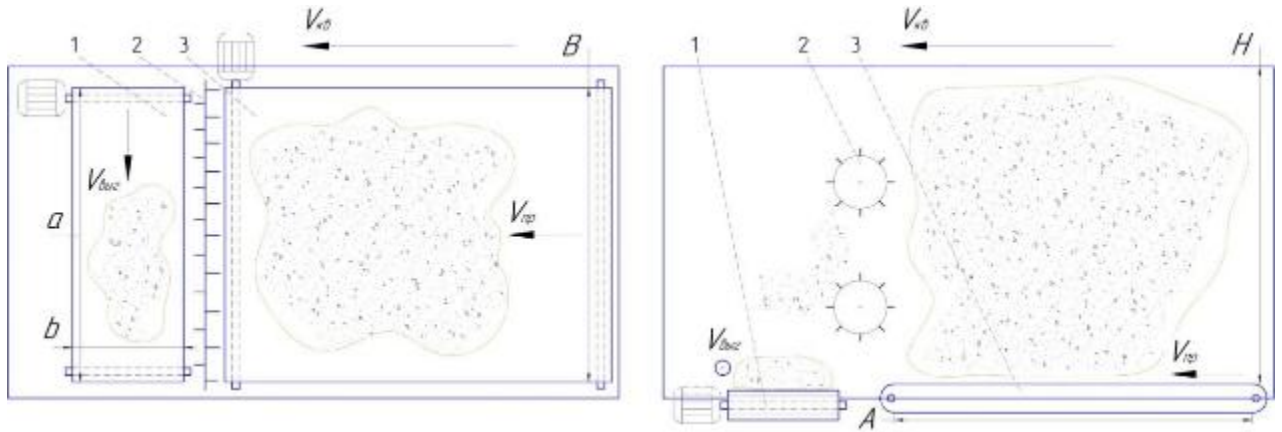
Схема кормового візка. Вид зверху (ліворуч) та вид збоку (праворуч): 1 - поперечний транспортер; 2 - бітерний механізм; 3 - поздовжній транспортер
